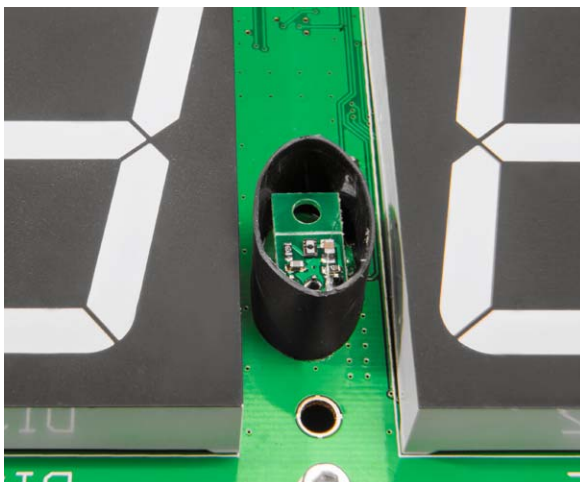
Montage des Helligkeitssensors mit Abdeckung aus Schrumpfschlauch
